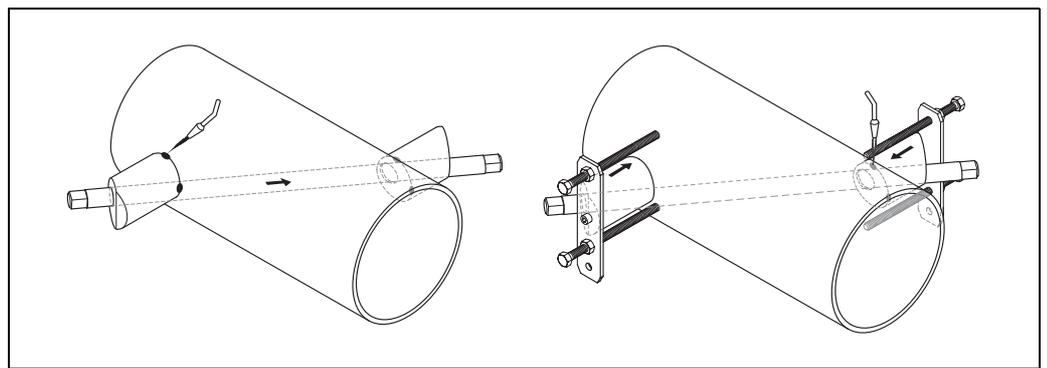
Montaggio dei sensori di misura, fasi 7 e 8
